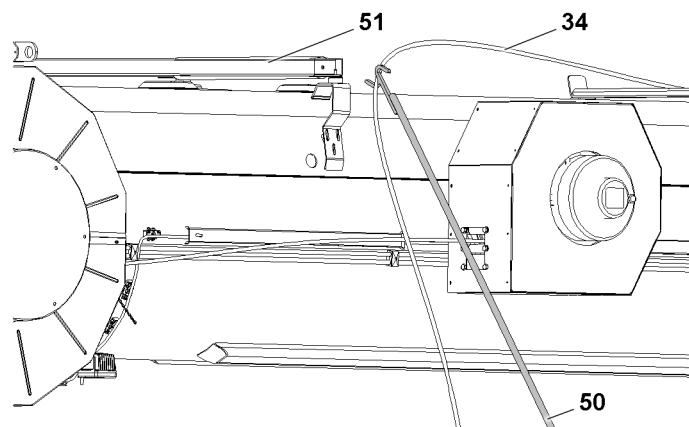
Guiar el cable auxiliar con la barra de montaje
